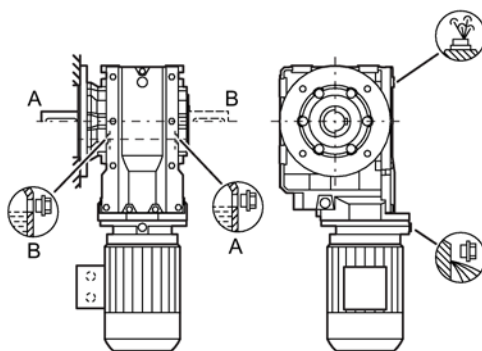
Монтажные положения для конического редуктора В.Ф в исполнении с фланцем и В.З с фланцем корпуса, типоразмер 19–29
